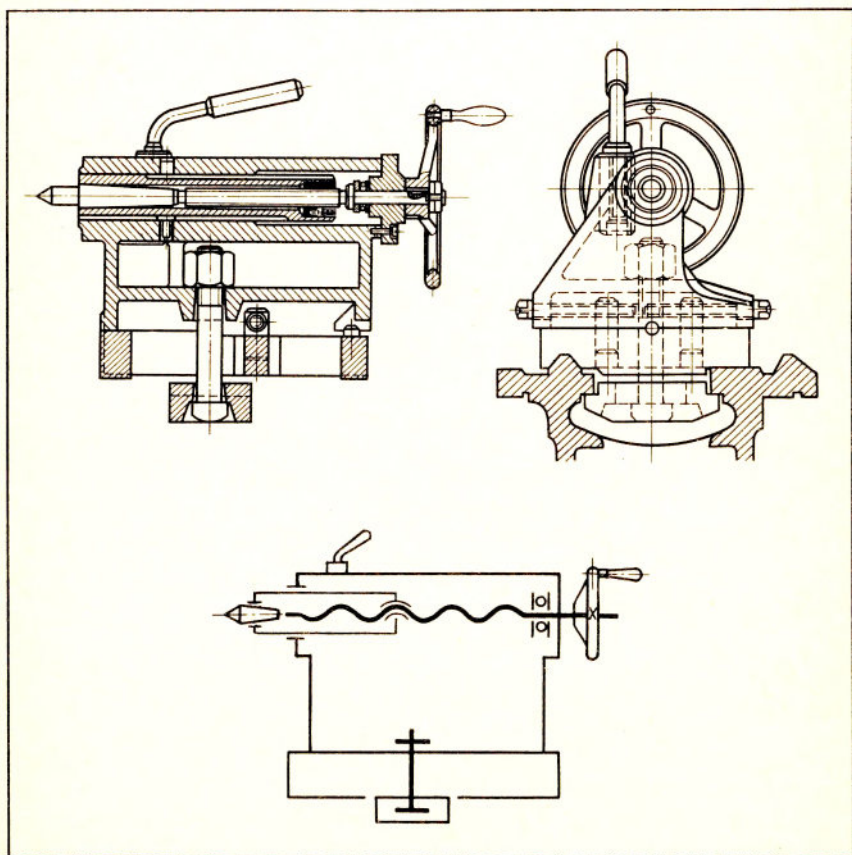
Сборочный чертеж и кинематическая схема задней бабки станка
